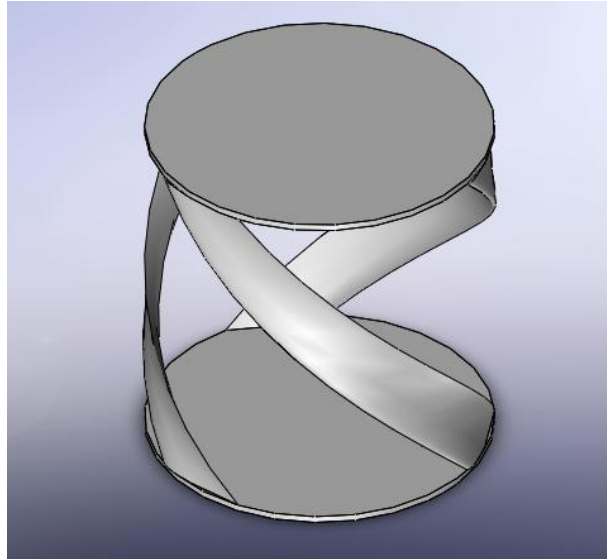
Diseño realizado en el software CAD SolidWorks con 3 álabes
